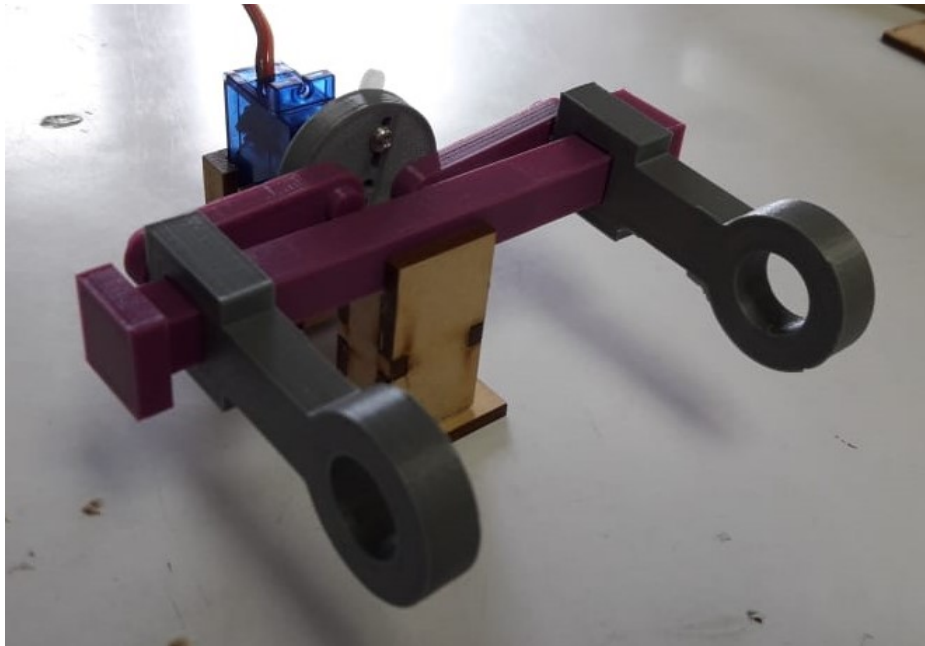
Vista frontal del mecanismo de posicionamiento manufacturado
